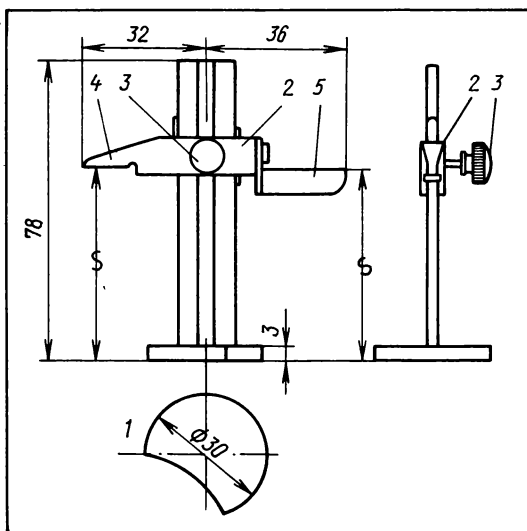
Шаблон для регулировки деталей лентопротяжного механизма:
